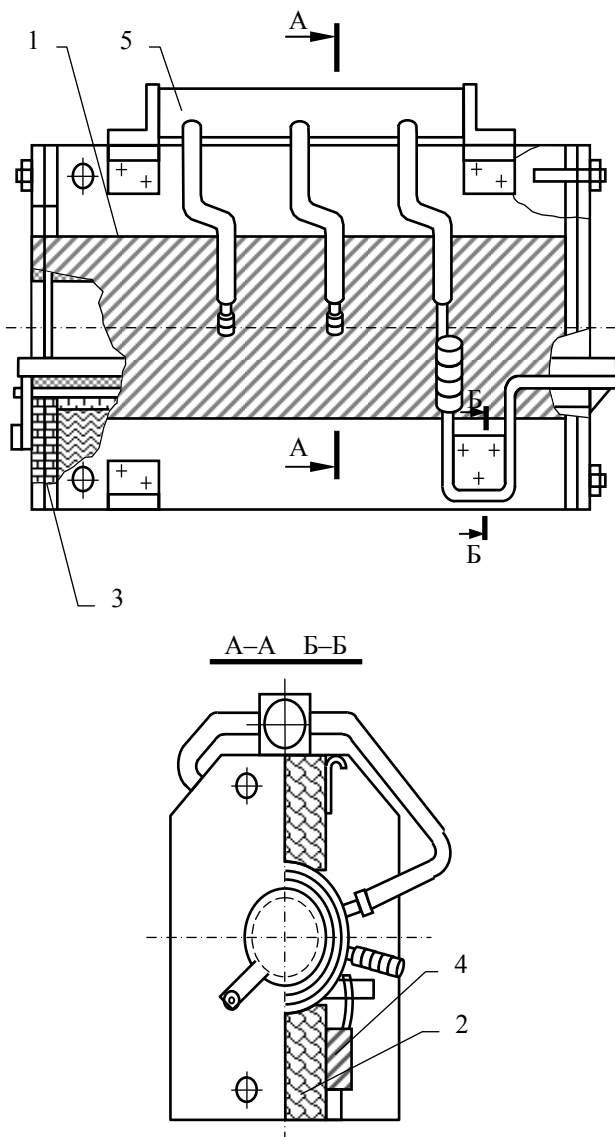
Многовитковый индуктор для сквозного подгрева кузнечных цилиндрических заготовок:
